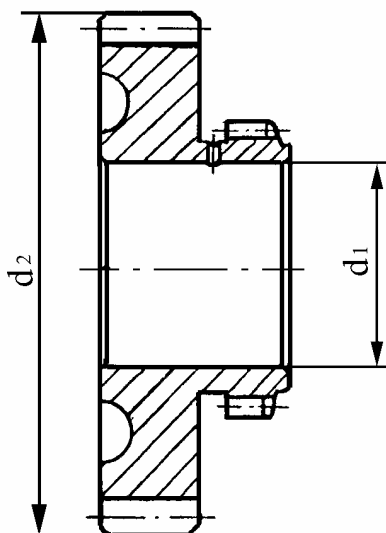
Шестерни высшей и низшей передач ведущего вала.
